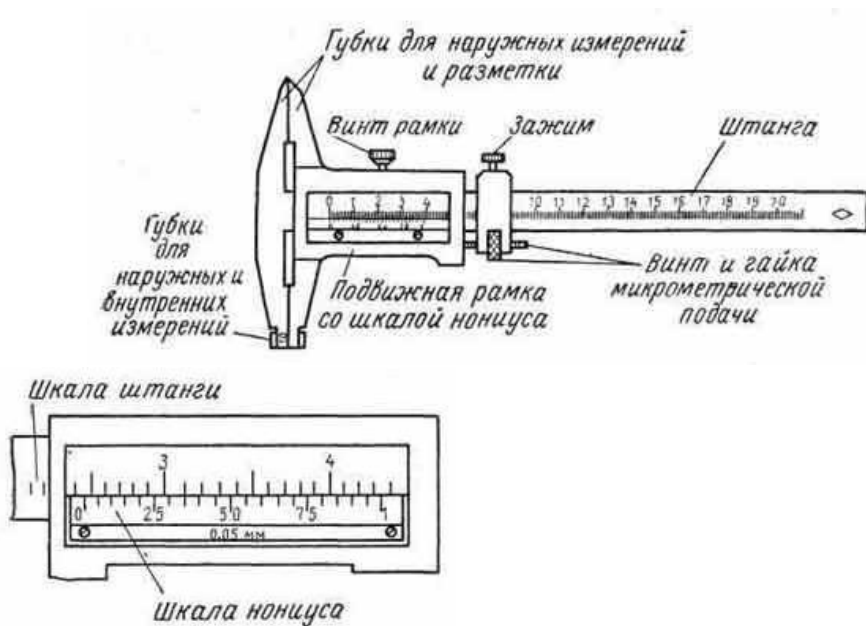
Конструкция штангенциркуля типа ШЦ-II
